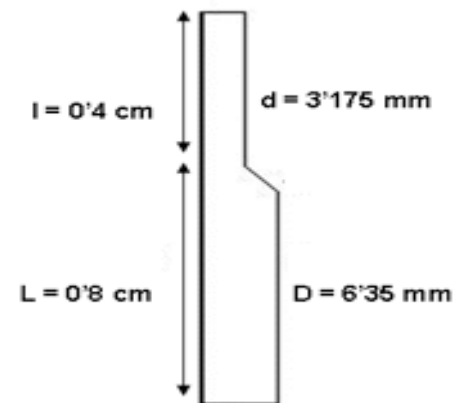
Esquema 2D y dimensiones del diseño de la cánula modificada.
